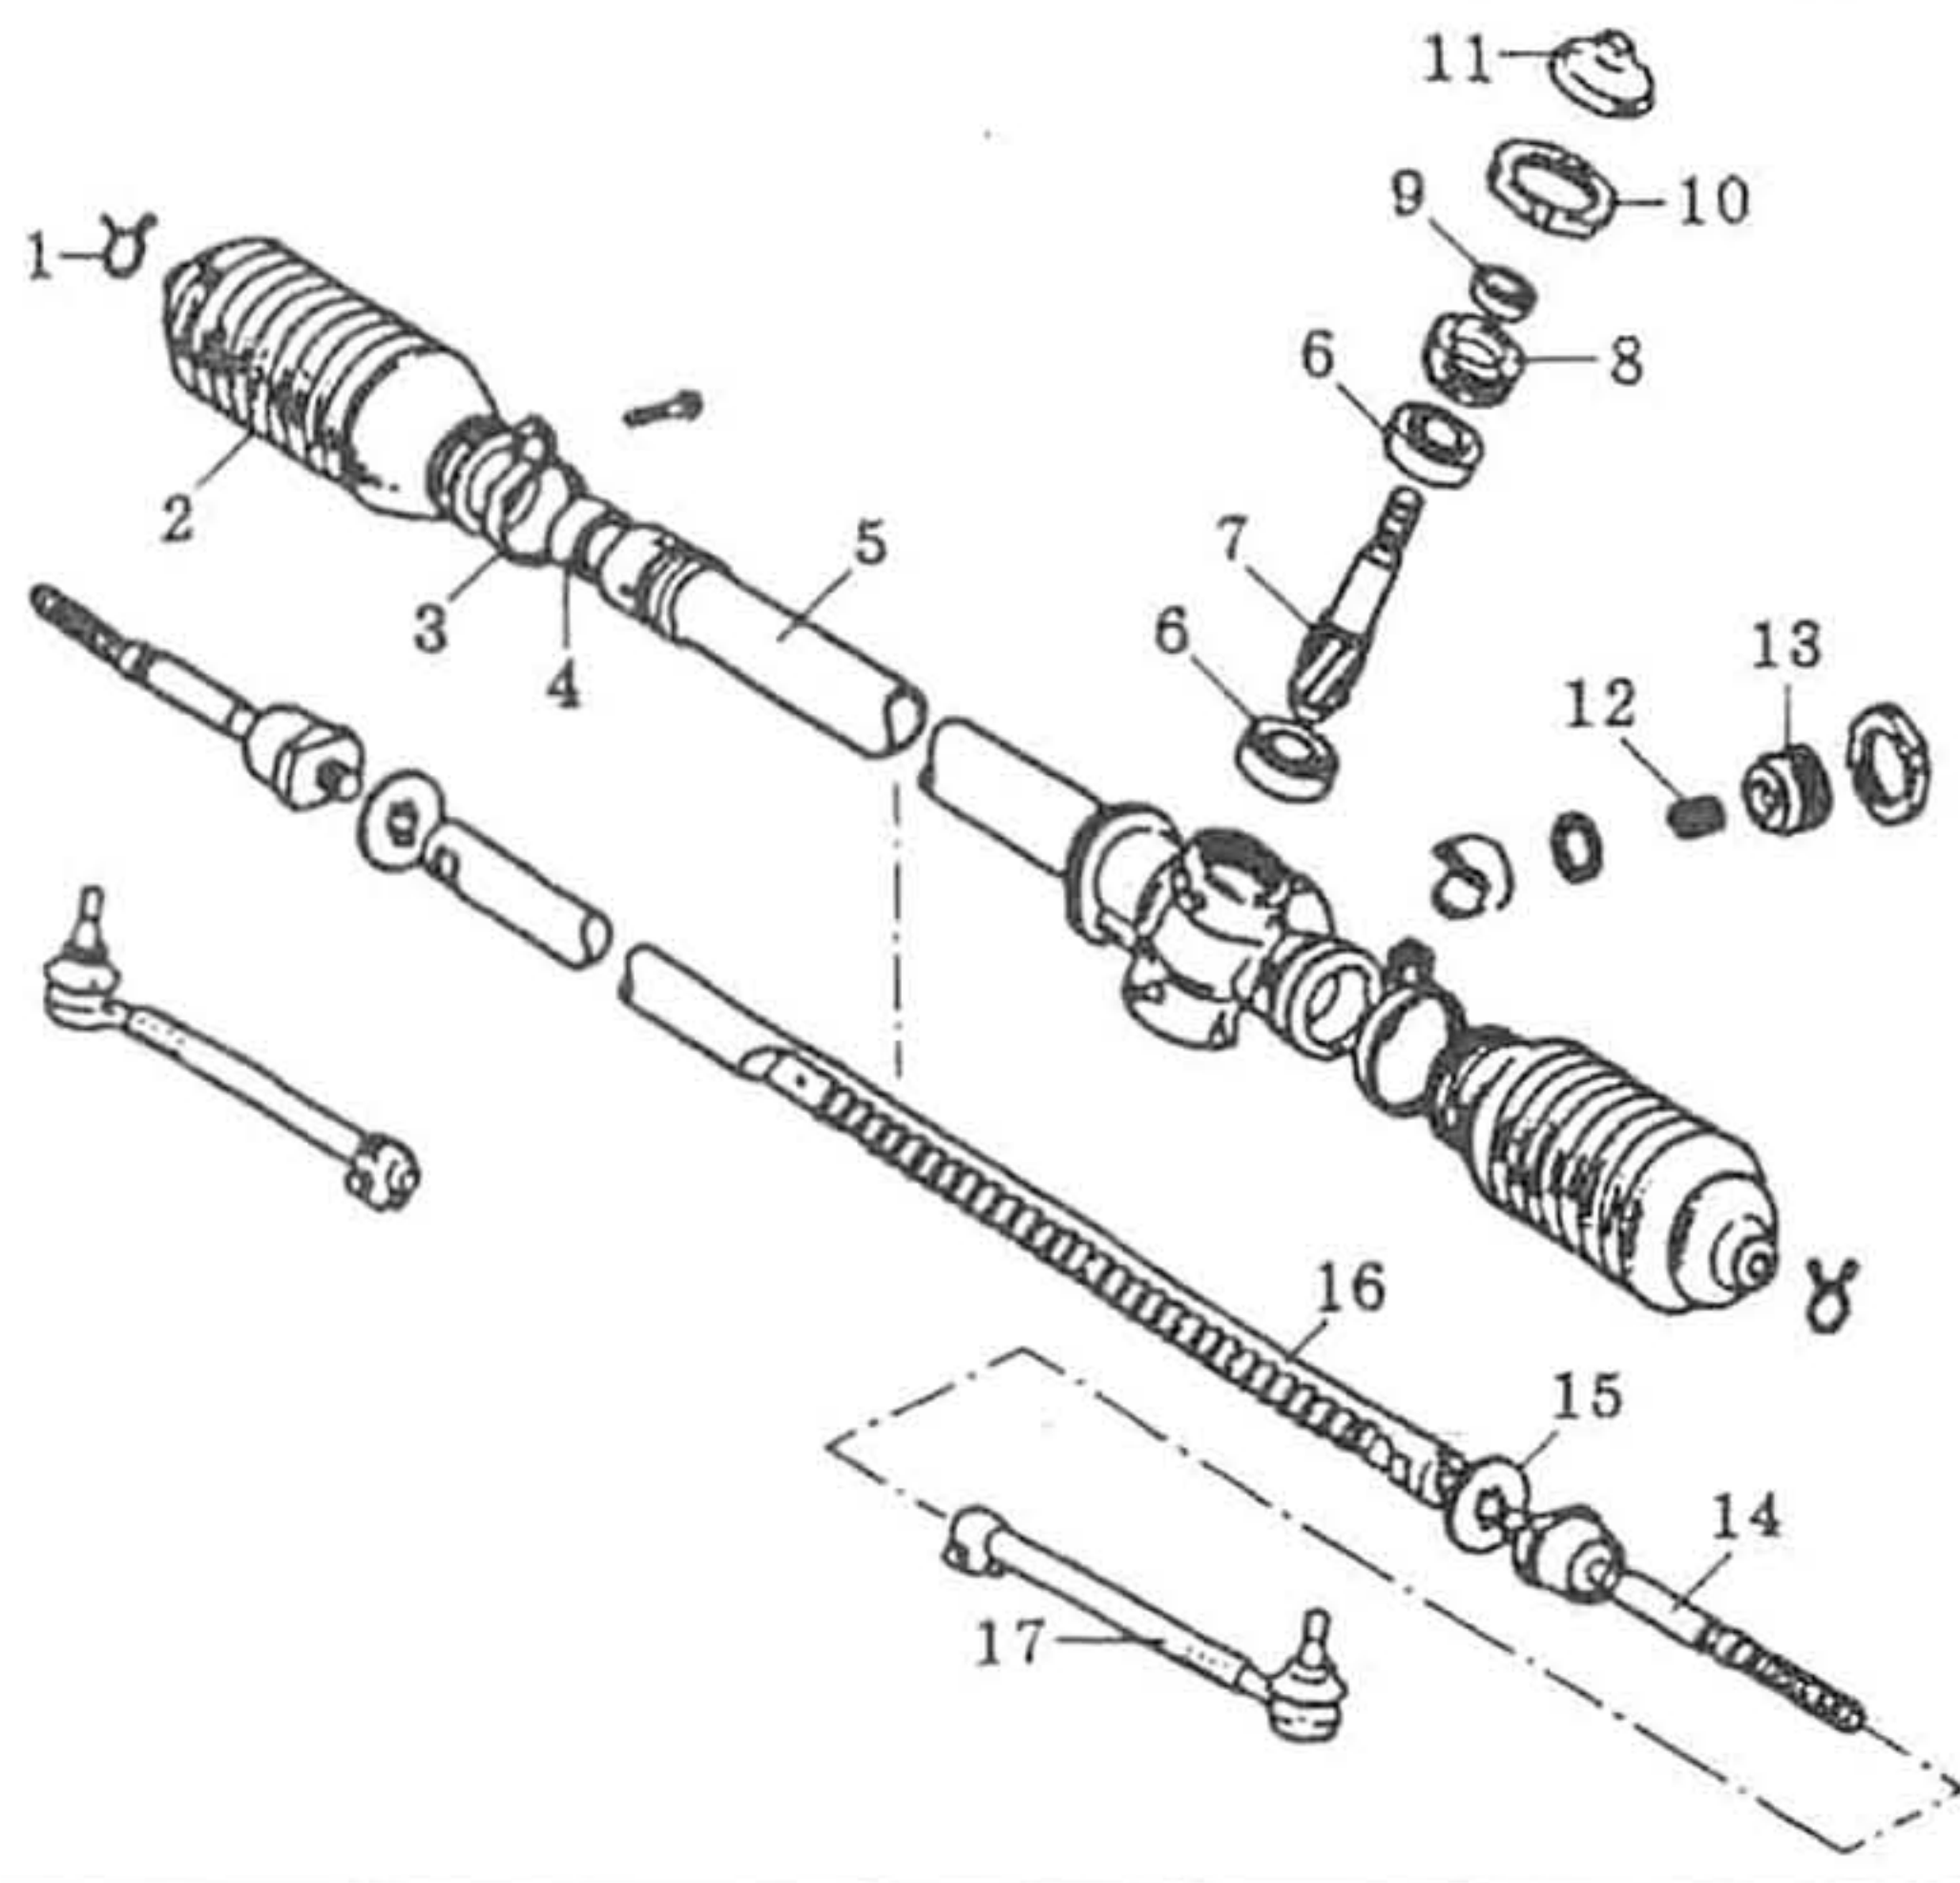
1. Зажим. 2. Чехол. 3. Хомут. 4. Втулка. 5. Корпус рейки. 6. Подшипник. 7. Червяк. 8. Регулировочный элемент. 9. Сальник. 10. Стопорная гайка. 11. Пылезащитная крышка. 12. Пружина. 13. Винт направляющей рейки. 14. Наконечник рейки (рулевая тяга). 15. Шайба с лепестками. 16. Рейка. 17. Наконечник рулевой тяги.
